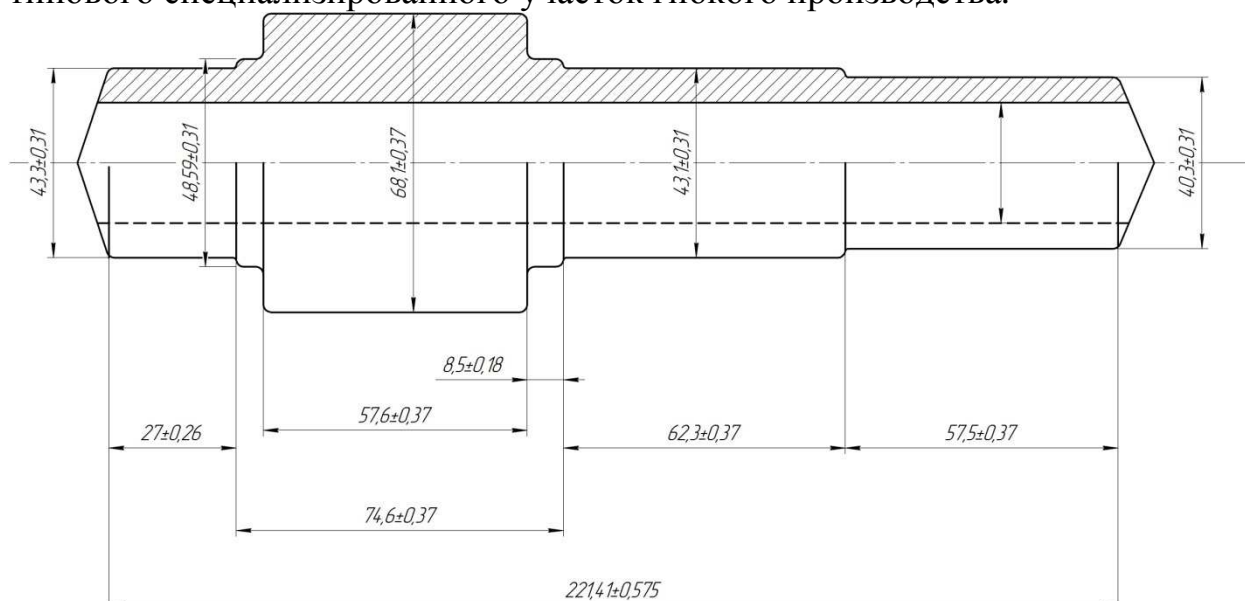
Вид рабочего чертежа индивидуальной детали тела вращения
